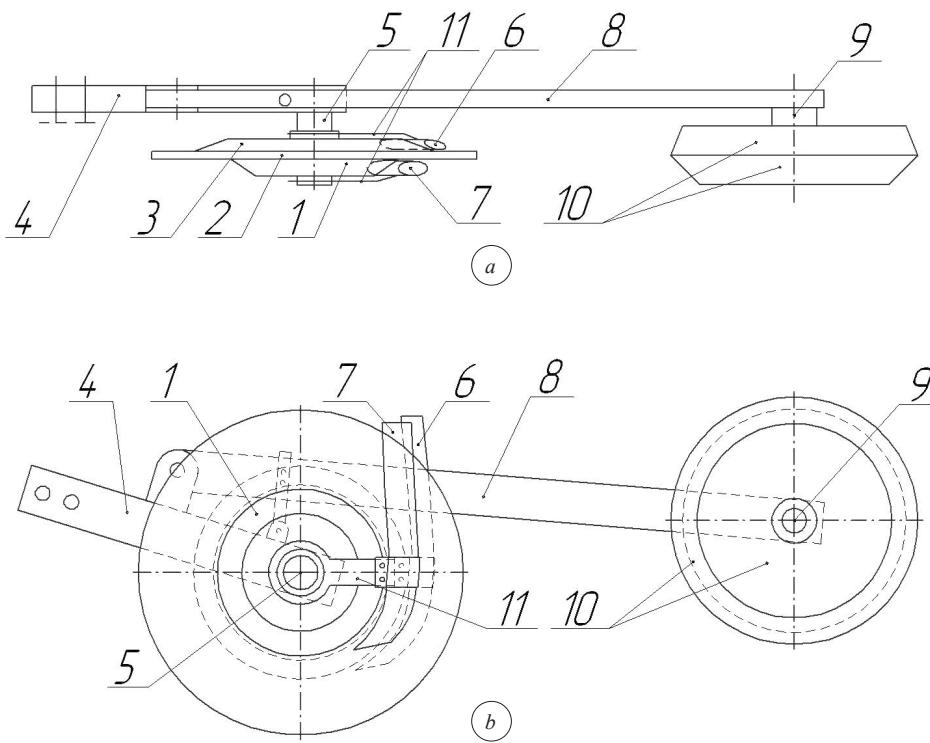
Комбинированный однодисковый сошник с двухсторонними ребордами-бороздкообразователями с разными диаметрами и нулевым углом атаки дисков: *a* – вид сверху; *b* – вид сбоку; 1 – уплотнители; 2 – плоский диск; 3 – уплотнитель; 4 – корпус; 5 – ось; 6 – семя направитель; 7 – туконаправитель; 8 – поводок; 9 – ось; 10 – прикатывающий каток; 11 – пластины
